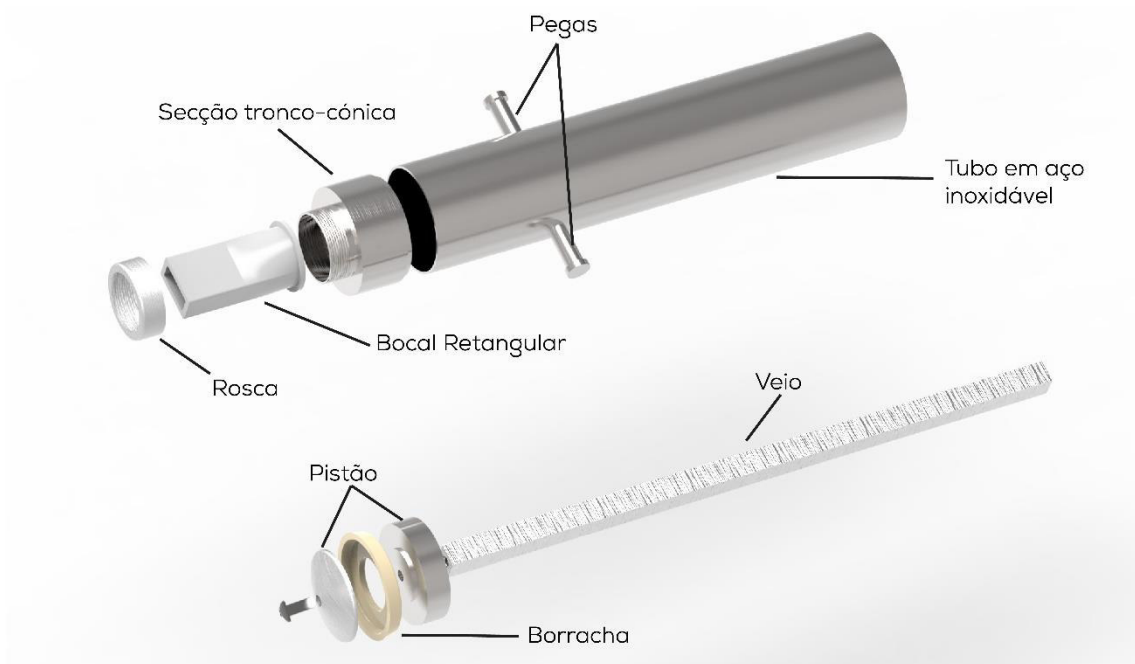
Vista explodida com componentes do novo extrusor.
